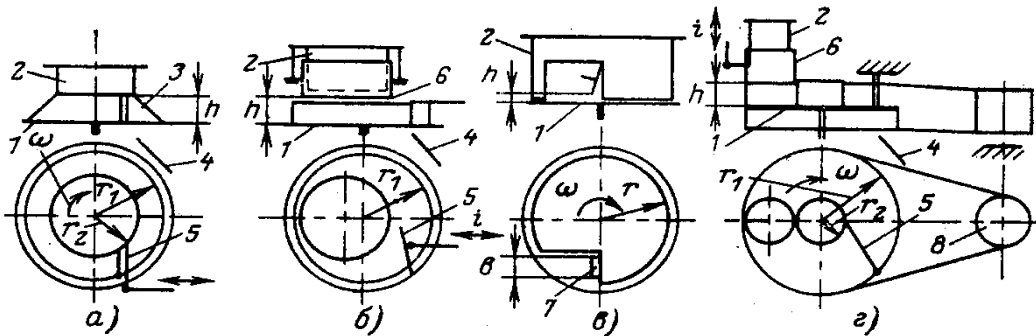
Схеми тарілкових і дискових дозаторів: а – з нерухомою конусною манжетою; б – з ексцентричною рухомою манжетою; в – з патрубком і обертовою заслінкою; г – з ексцентричною рухомою манжетою і гнучкою стінкою; 1 – таріль; 2 – циліндричний патрубок; 3 – конусна манжета; 4 – лоток; 5 – ніж; 6 – рухома манжета; 7 – заслінка; 8 – шків
